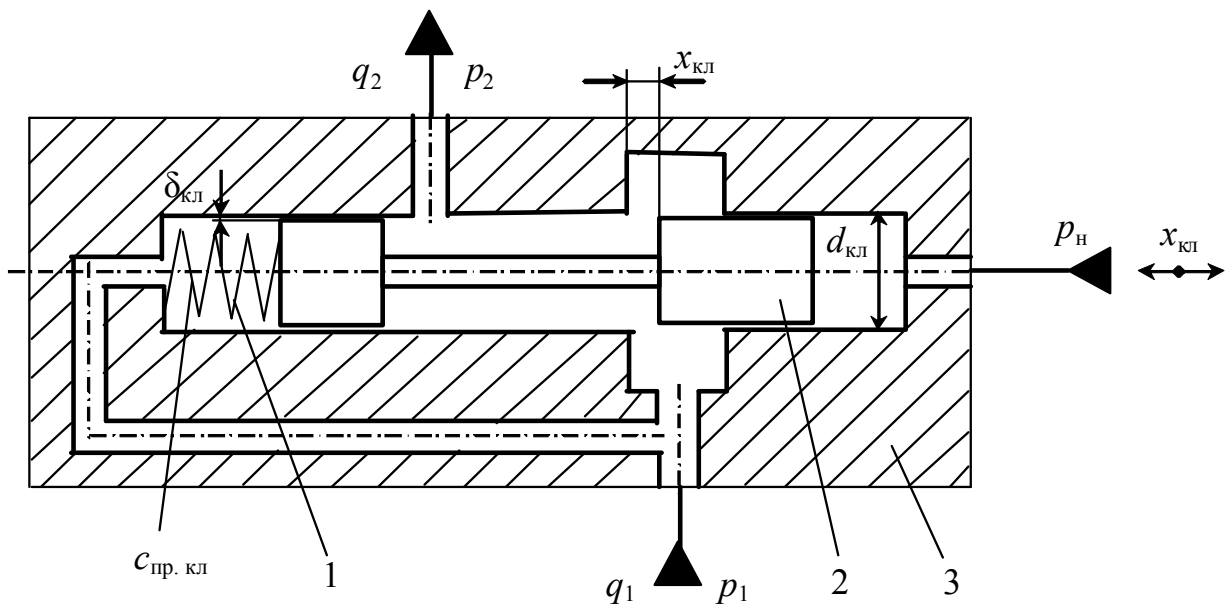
Розрахункова схема клапана тиску: 1 – пружина; 2 – ЗРЕ; 3 – корпус
